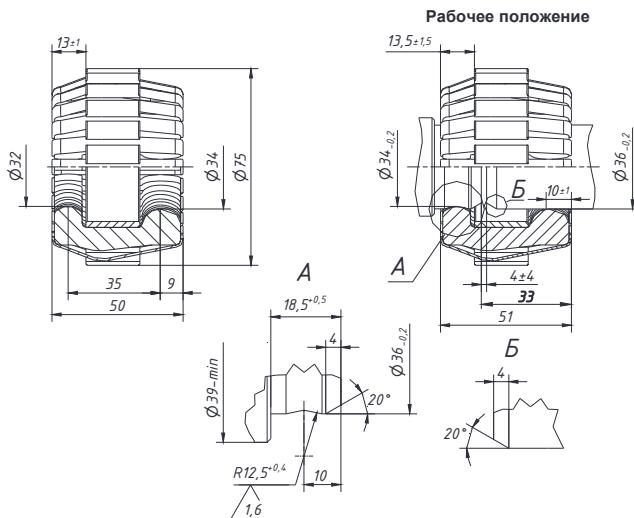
Габаритные и присоединительные размеры розеточных контактов типа KP/TEL
